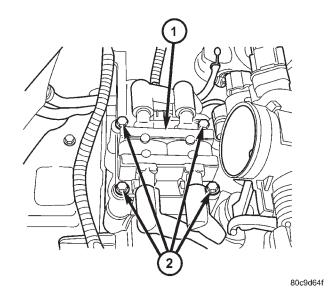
BOBINA DE ENCENDIDO - 2.4L
